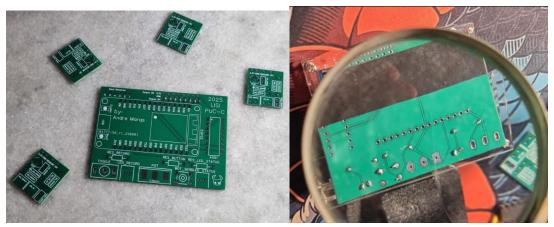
Placas desenvolvidas após recebimento || Mobos sendo soldadas.
